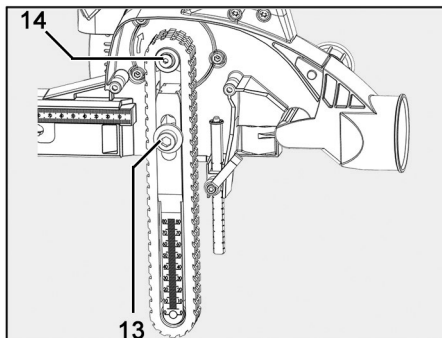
Montaje y desmontaje de la rueda de cadena, cadena de fresar y riel guía
